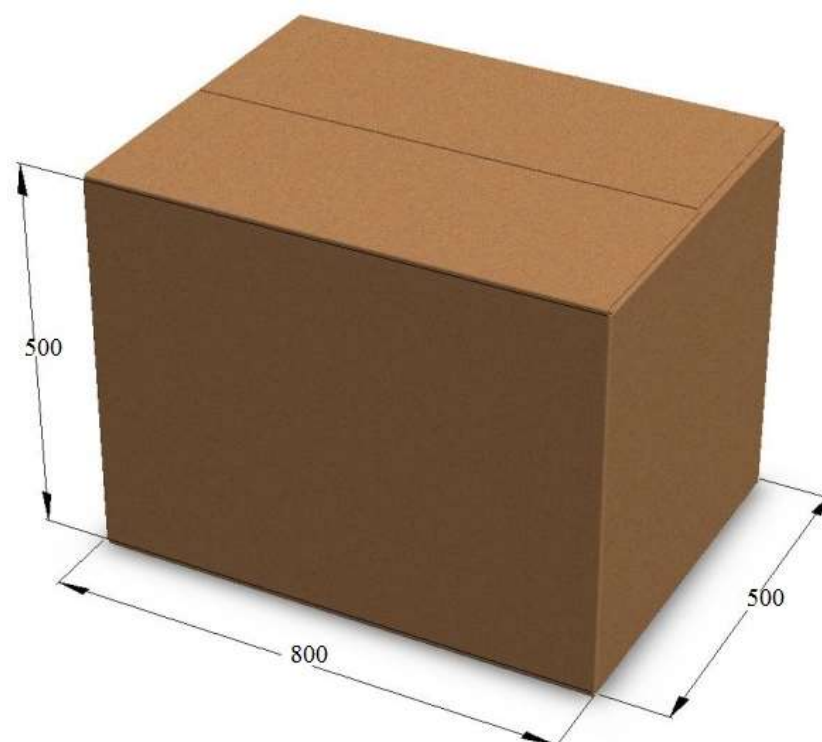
Образец упаковки шприцов в коробки 800/500/500
